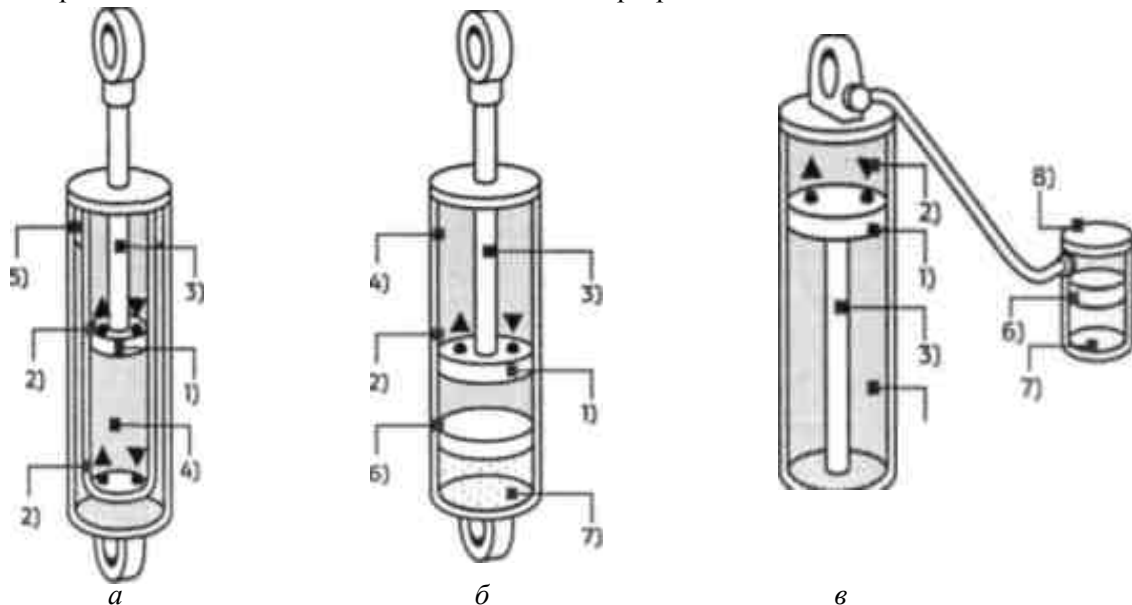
Амортизатори з газовим підпором: а – двотрубний; б – однострубний; в – амортизатор Ohlins з додатковим резервуаром.
